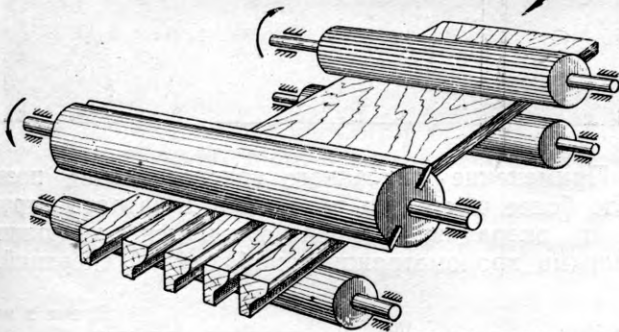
Схема окончательной обработки деталей на рейсмусном станке (вторая операция)
